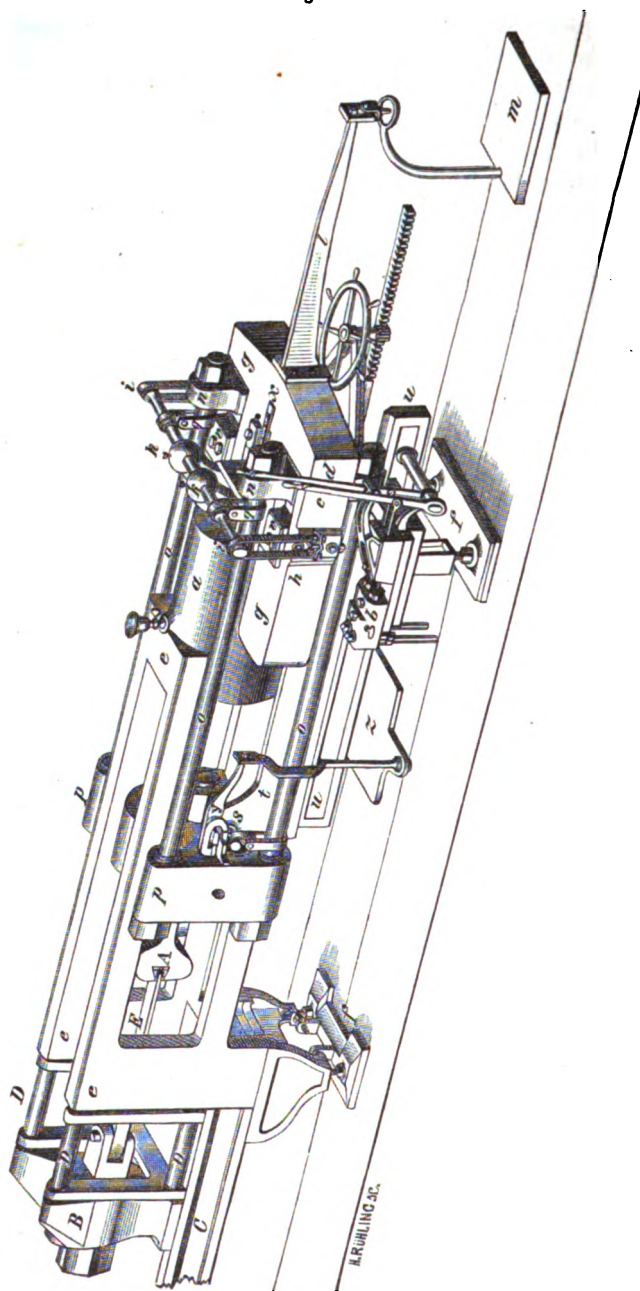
ist der Press-Cylinder der hydraulischen Presse der Maschine; in dem Messing-Gussstück b liegen die Cylinder zweier zugehöriger Druckpumpen, die das Wasser mittelst Gummischläuchen aus einem untergestellten Reservoir entnehmen und durch ein, in der Figur nicht sichtbares Verbindungsrohr von Kupfer in den Press-Cylinder drücken. Der 2,6 Zentimeter dicke Kolben der einen Druckpumpe wird durch den Hebel c in Bewegung gesetzt, dessen Uebersetzungsverhältnisse 1 : 4,2 ist, es kann damit ein Mann bequem eine Kraft von 20 Tonnen am Presskolben ausüben. Darüber hinaus, wird der Hebel d mit dem Uebersetzungs-Verhältniss 1 : 5,5 verwendet, der den nur 0,96 Zentimeter dicken Kolben der zweiten Druckpumpe bewegt; mit diesem kann die auszuübende Kraft mit Leichtigkeit auf 90 Tonnen gesteigert werden. Alle bisher genannten Theile sitzen an dem festen Gestelle e der Maschine, das mittelst geeigneter Füße auf den Fundamentplatten f f ruht.
